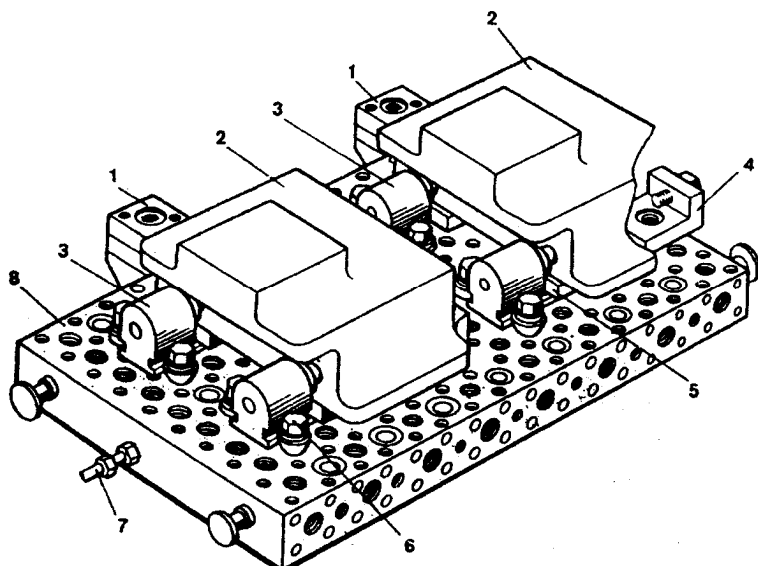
Двухместное приспособление для установки заготовок корпусной детали:
